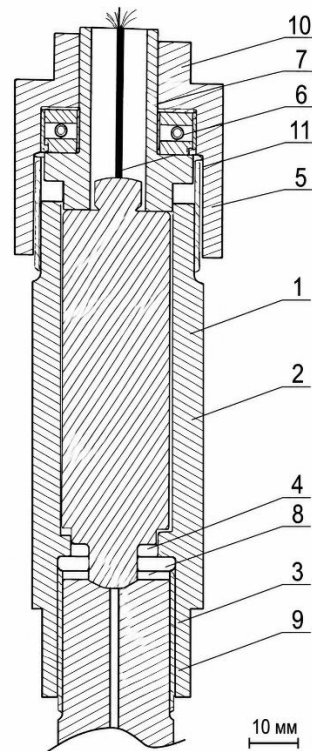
Притискний пристрій для автономних клапанних камер високого тиску: 1 – корпус, 2 – камера високого тиску, 3 – квадратний отвір, 4 – притискна гайка, 5 – опорний підшипник, 6 – п'ята, 7 – штуцер камери, 8 – шестигранник, 9 – штуцер УВД-15000.
